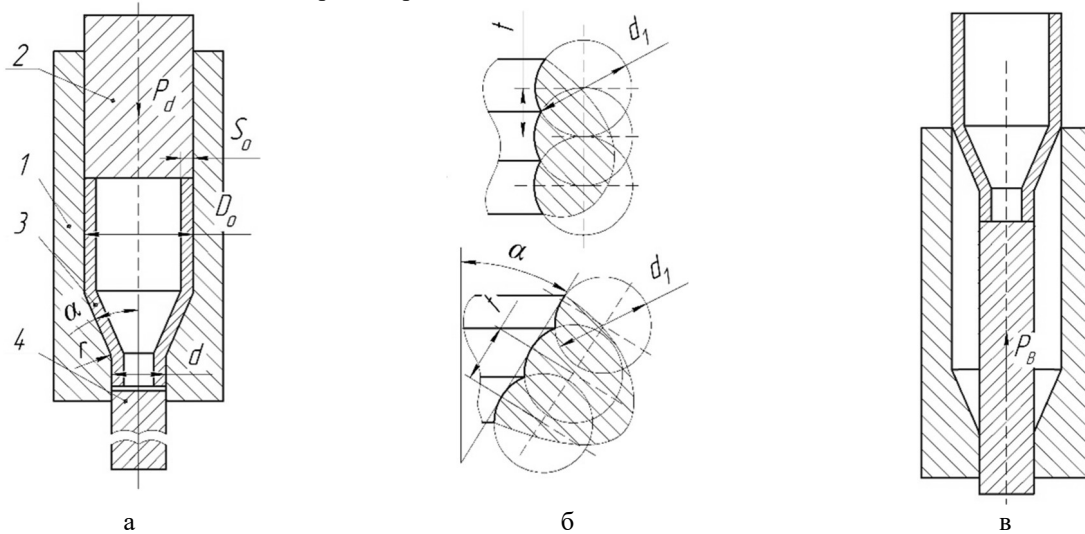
Схеми формоутворення виробу з горловиною закритим обтиском трубчастих заготовок в конусній матриці: а – схема закритого обтиску, б – форма циліндричної та конусної деформуючої поверхні матриці спеціального профіля, в – схема виштовхування виробу із матриці
